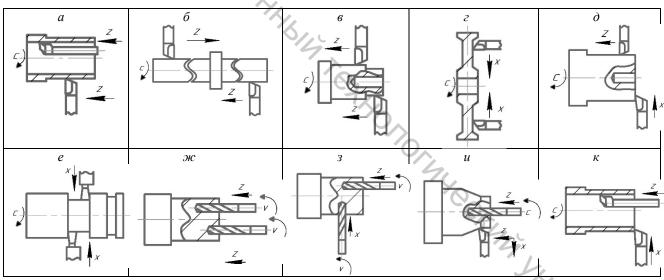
Примеры одновременных работ инструментами разных револьверных головок (а – обтачивание и растачивание; б – обтачивание в противоположных направлениях; в – обтачивание в одном направлении; г – обработка торцов; д – обтачивание и подрезка торца; е – точение канавок и пазов с радиальной подачей; ж – продольная обработка двумя осевыми инструментами; з – продольная и поперечная обработка двумя осевыми инструментами; и – продольная обработка осевым инструментом и обтачивание; к – растачивание и подрезка торца)
